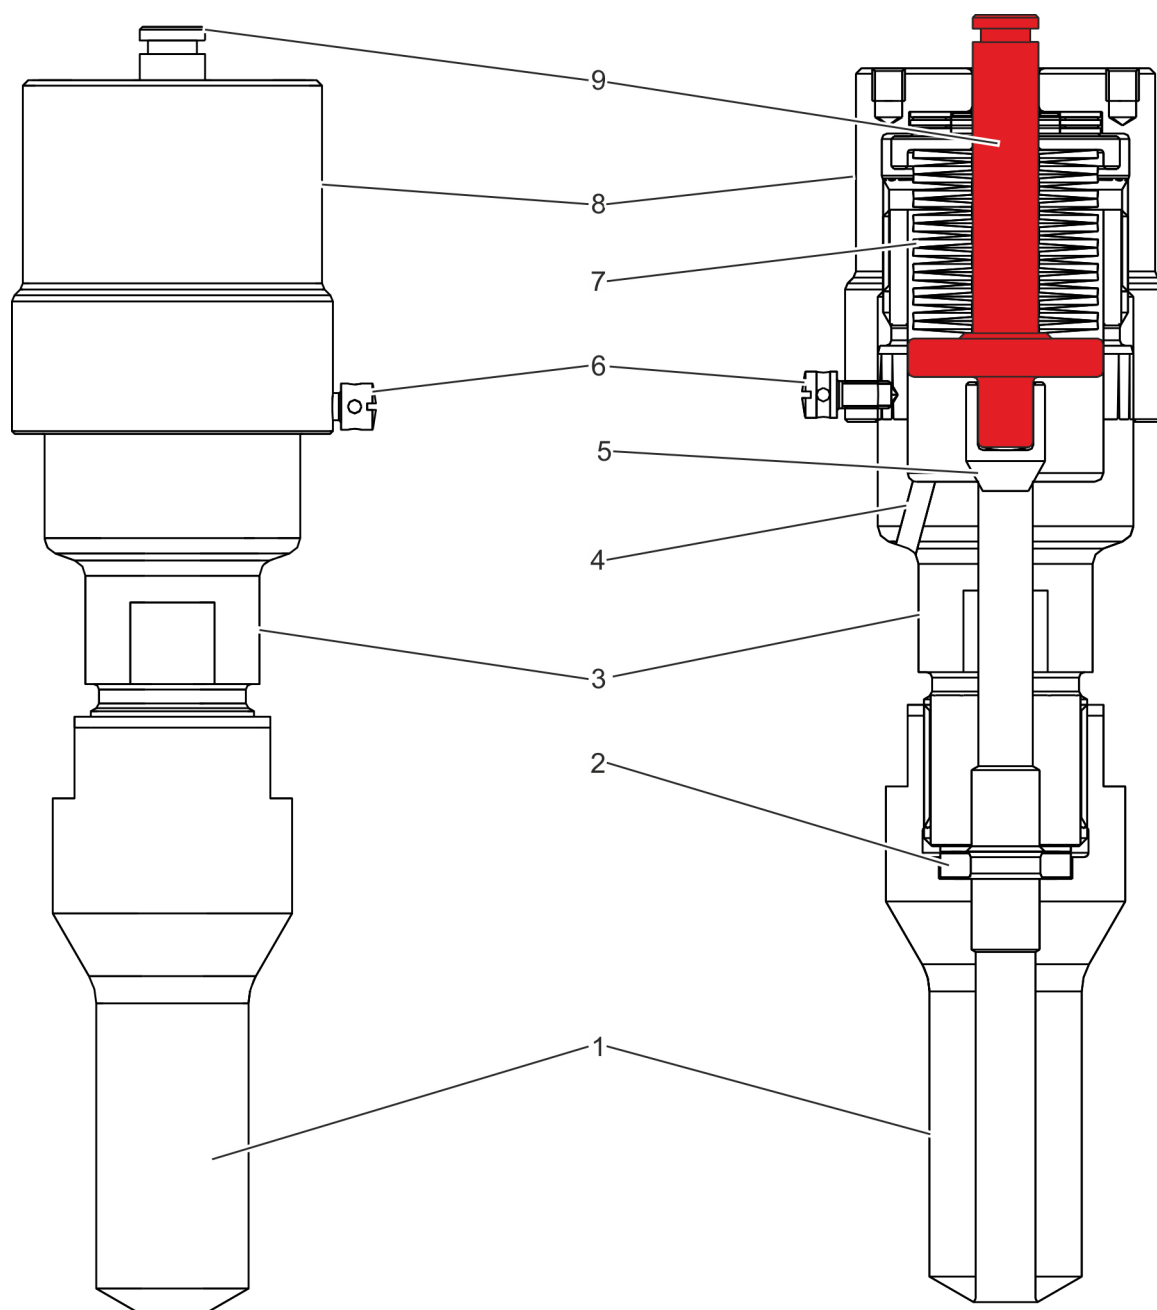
Vue d'ensemble (à gauche) et vue en coupe (à droite)
